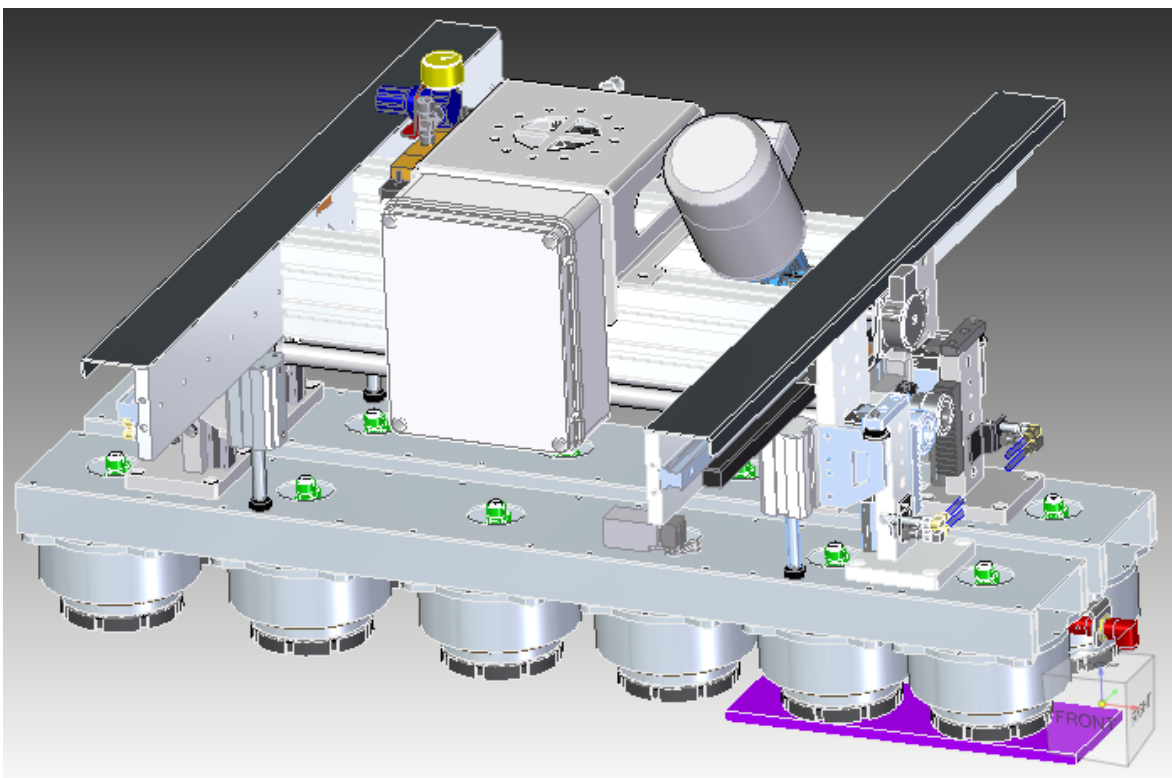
Sistema di presa a vuoto assemblato con dimensioni del pannello movimentabile minimo in viola
